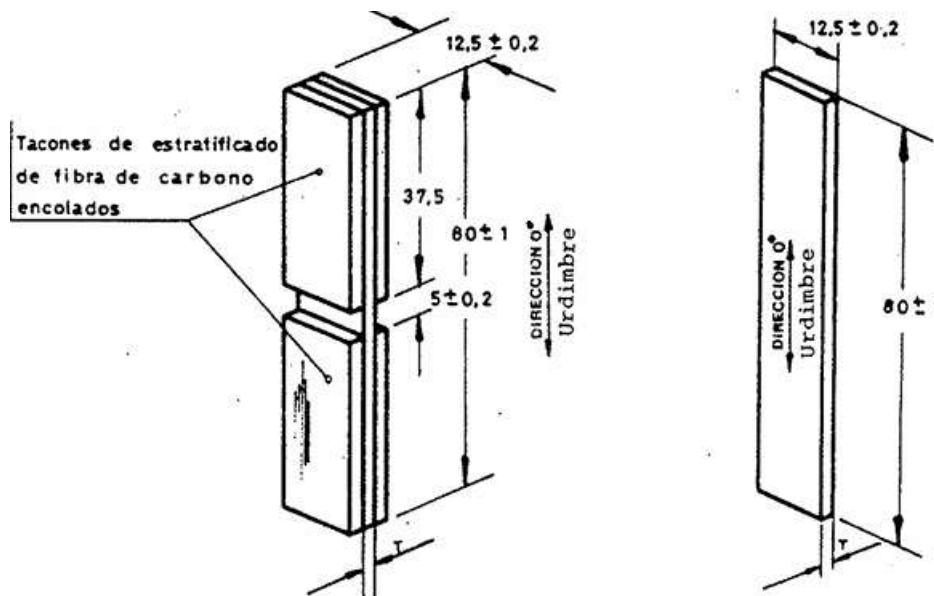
Dimensiones probeta norma I+D+E-51 [8].
